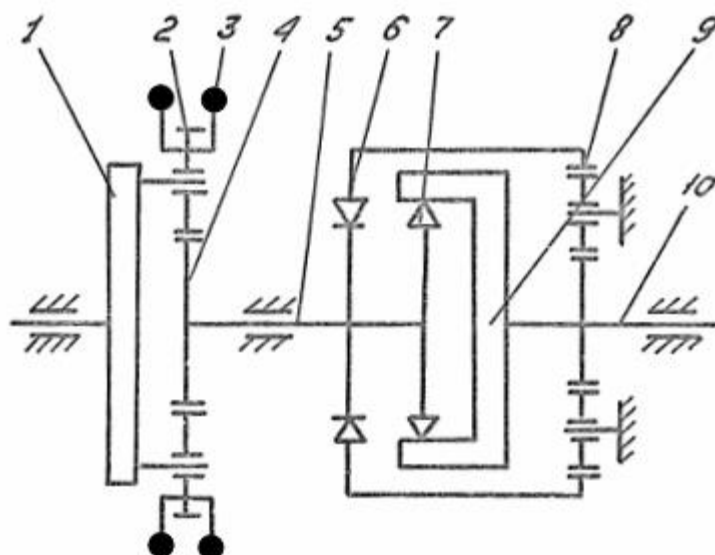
Схема инерционной передачи с реверсивной зубчатой передачей
